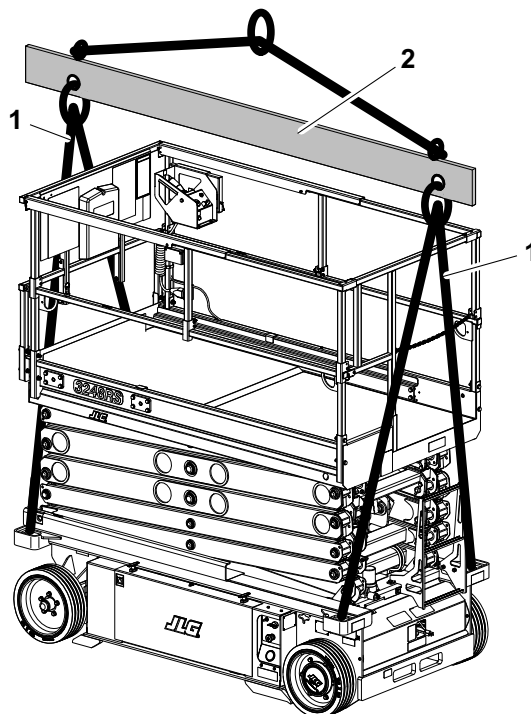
Elevação com Barra de Extensão e Localização dos Olhais de Elevação - Todas as Máquinas
